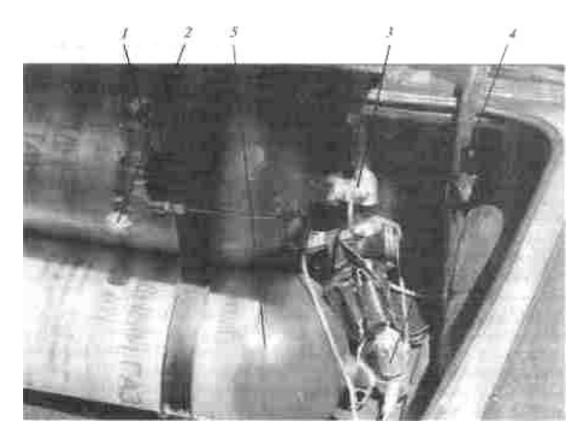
Монтаж арматуры баллонов СПГ: 1 — заправочное устройство; 2 — заправочный вентиль; 3 и 4 — баллонные вентили; 5 — баллон.
